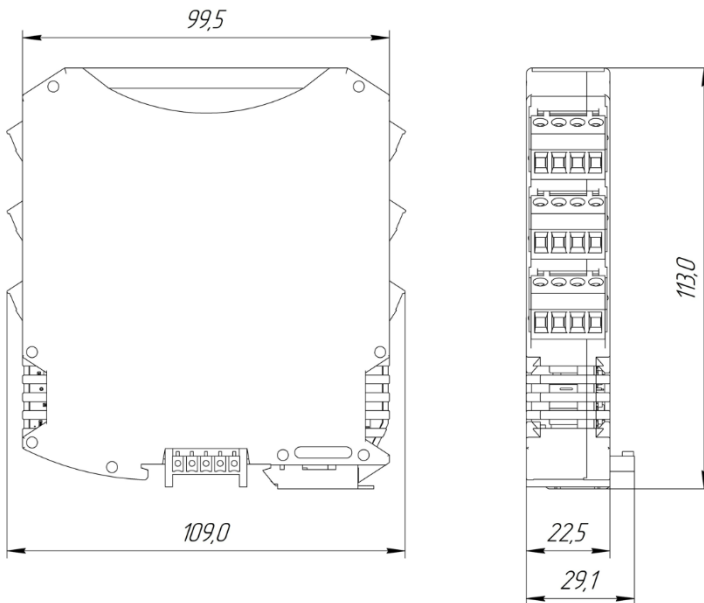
Габаритный чертеж преобразователя в стандартном корпусе
